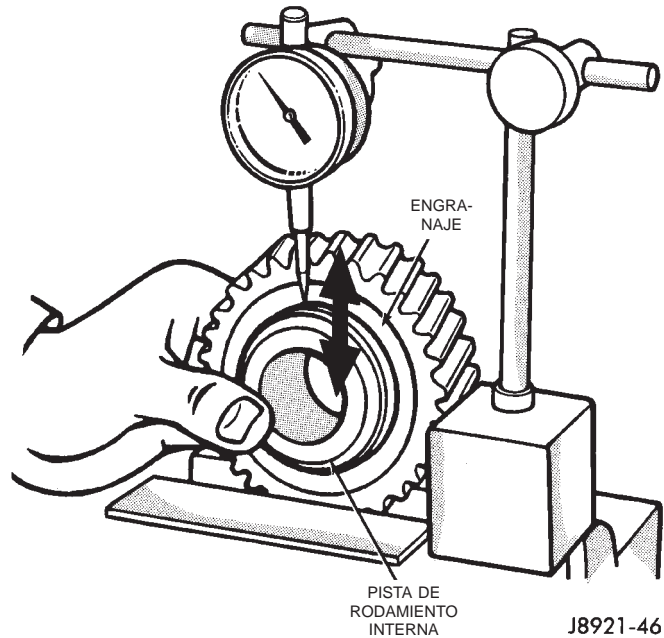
Verificación de holgura entre engranaje y pista de rodamiento
